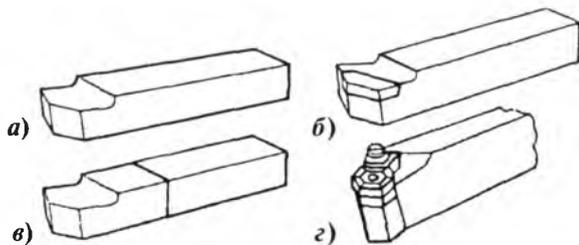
Типы токарных резцов по конструкции: цельные (а, б), составные с припаянными пластинами (в) или с механическим креплением пластин (г)
